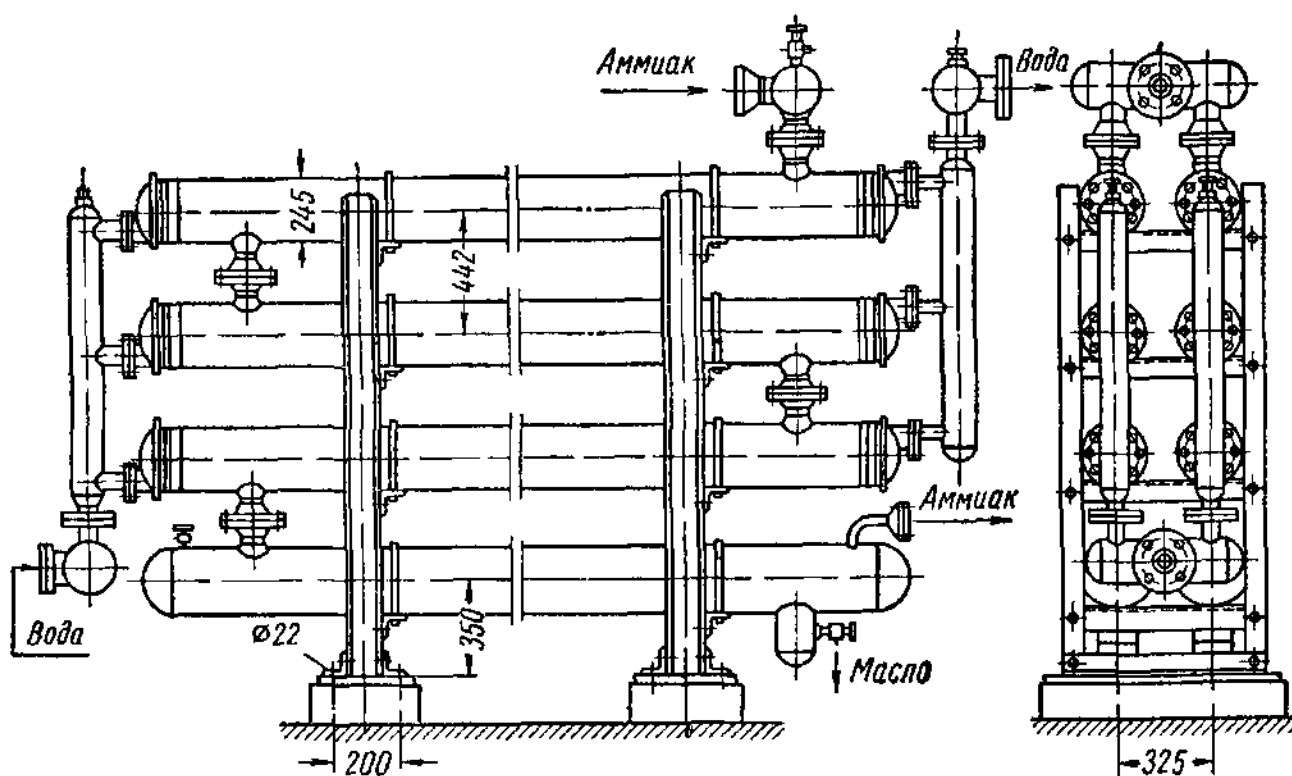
Двухходовой четырнадцатитрубный элементный конденсатор
